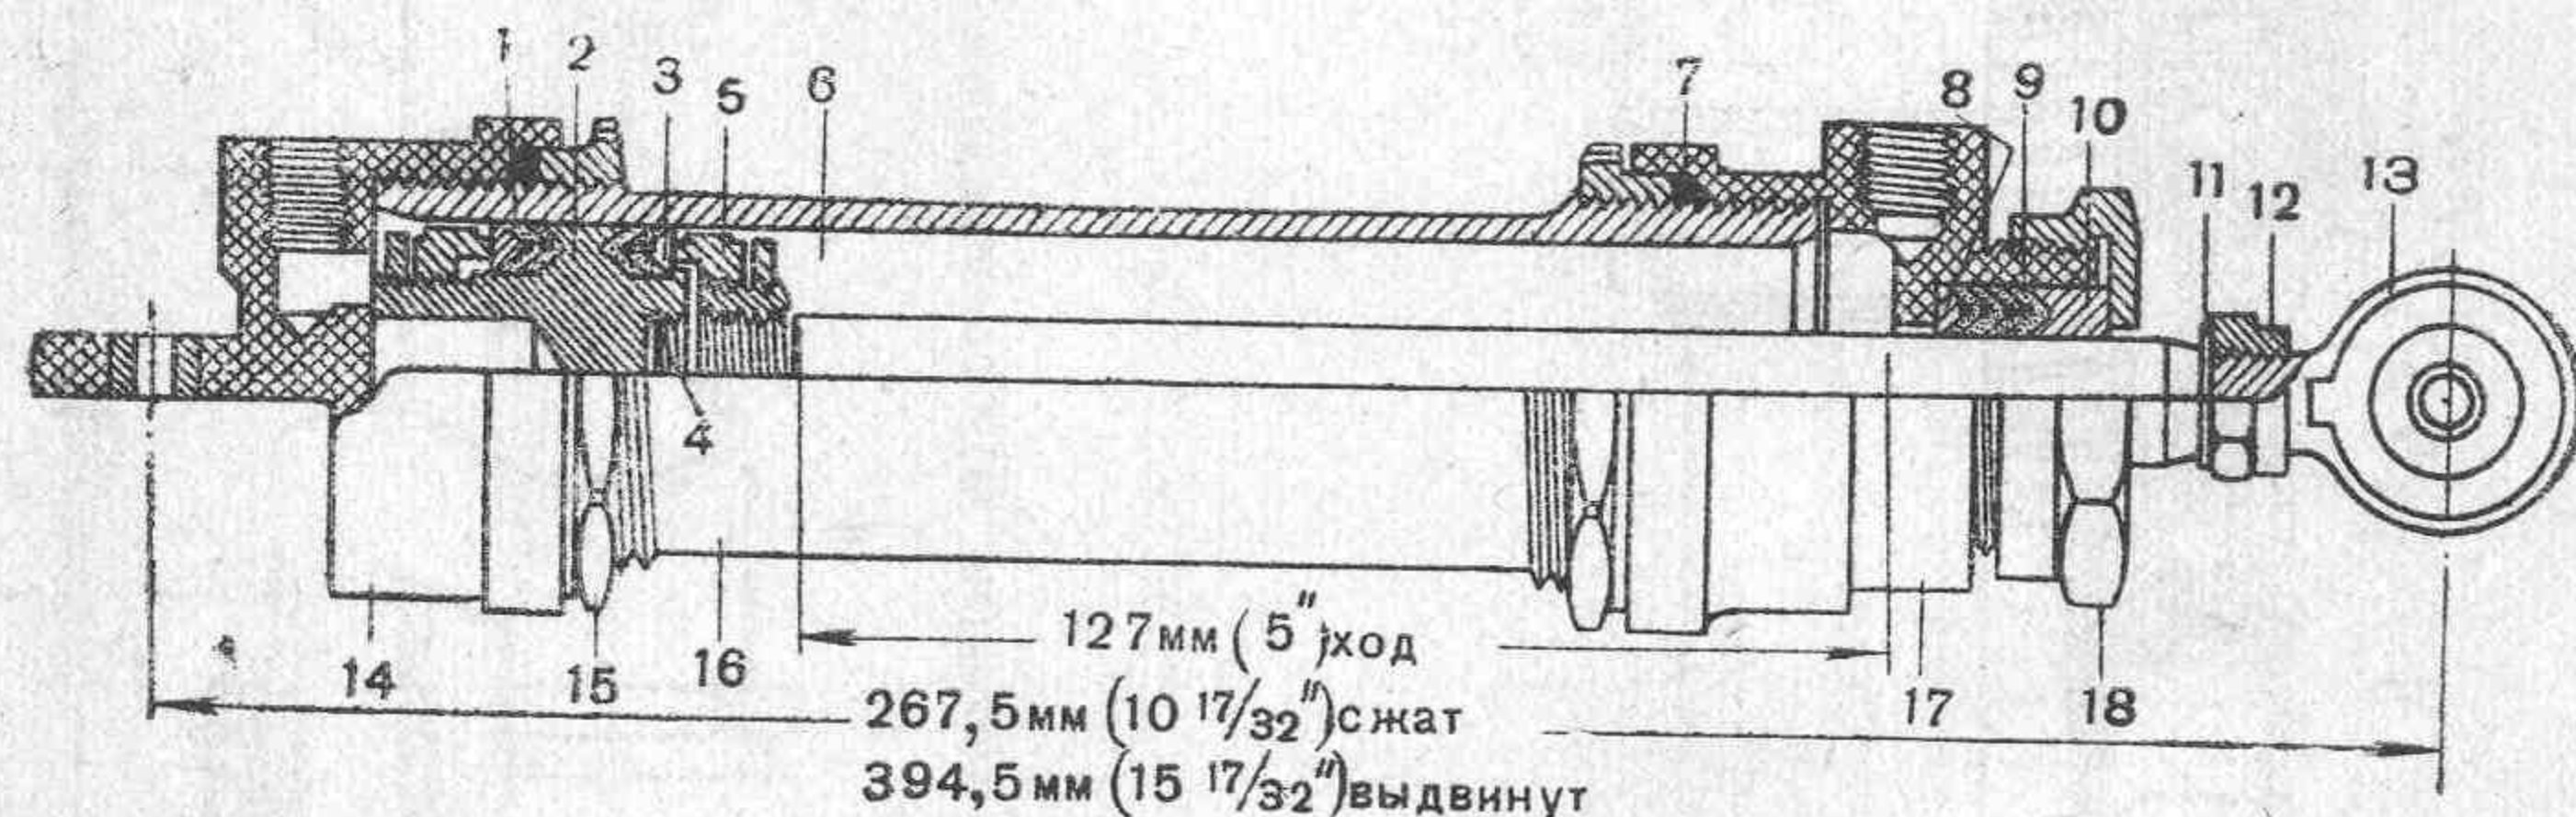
Силовой цилиндр подъема нижних юбок капота:
